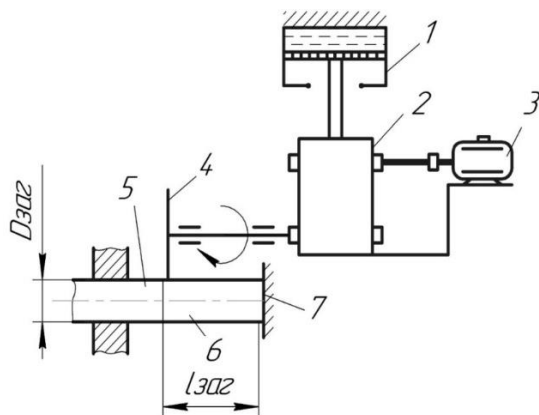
Схема резки прутков дисковыми пилами на ножовочно-отрезном станке
